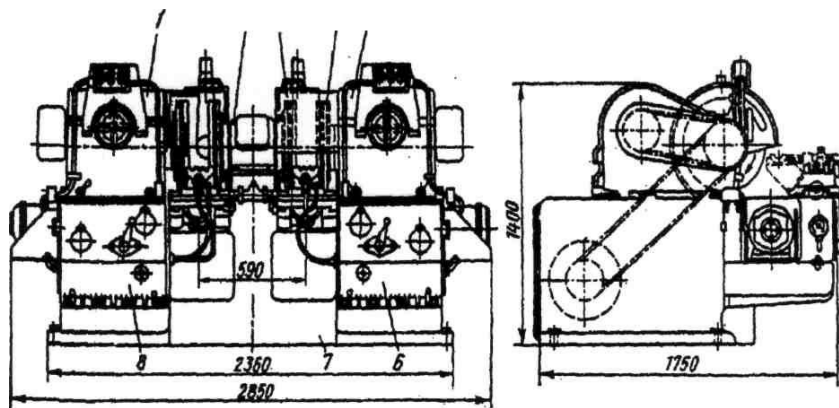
Напівавтомат для копіювально-шліфувальної обробки виливків: 1, 2, 5 - шліфувальні головки; 3 - супорт затиску 4 - супорт подачі; 6,8 - коробки гідроприводу; 7 - станина з приводом
